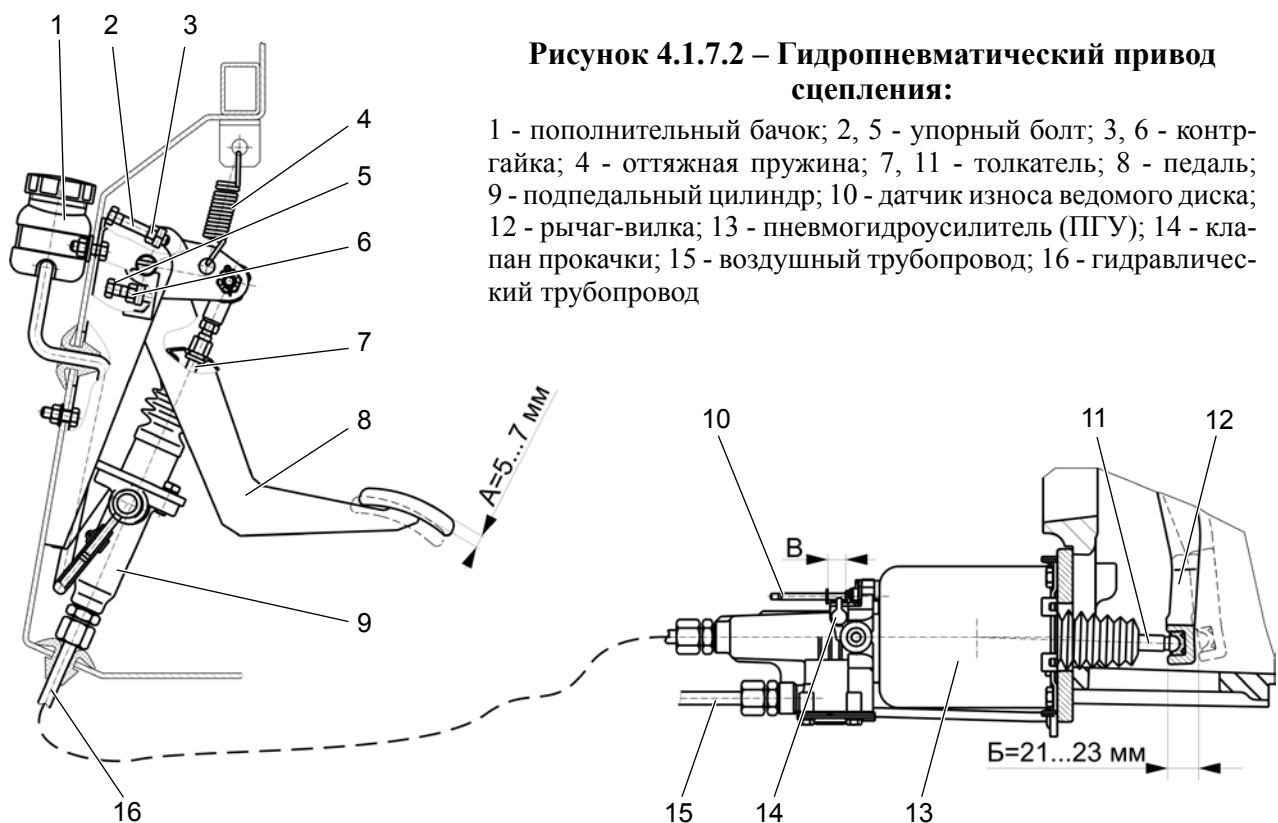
Гидропневматический привод сцепления:
